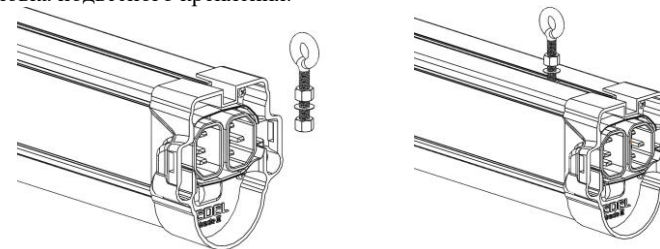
Вставка подвесного крепления в специальный паз на корпусе светильника
